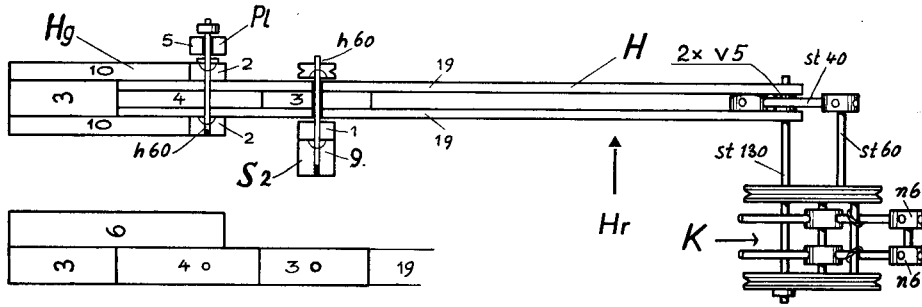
Der Hebel H Der Teil Hg bildet ein Gegengewicht für den Korb K. Die Befestigung des Korbes erfolgt mit einem auf 130 mm Länge zugeschnittenen Verbindungsstab st 130, ferner durch einen 60 mm langen Stab st 60. Dieser Stab steckt in einer Nabe, die mit einem 40 mm Stab st 40 mit dem Hebel verbunden ist. Der Stab st 40 liegt auf 2 Vorsteckern (2 x V5), die sich zwischen den beiden 19er Streben befinden. Auf diese Art hat der Stab st 40 die richtige Lage, wodurch auch der Korb K die richtige Lage erhält. Ein kleiner Pfeil kennzeichnet die Stelle, wo das 15 mm Rad Hr (doppelter Vorstecker) am Hebel angebracht wird. Es ist das das fünfte Loch vom Hebelende nach links gezählt.
